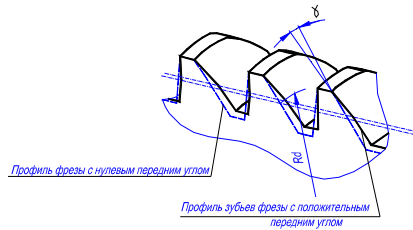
Схема расположения кромок фрезы с нулевым и положительным передними углами
